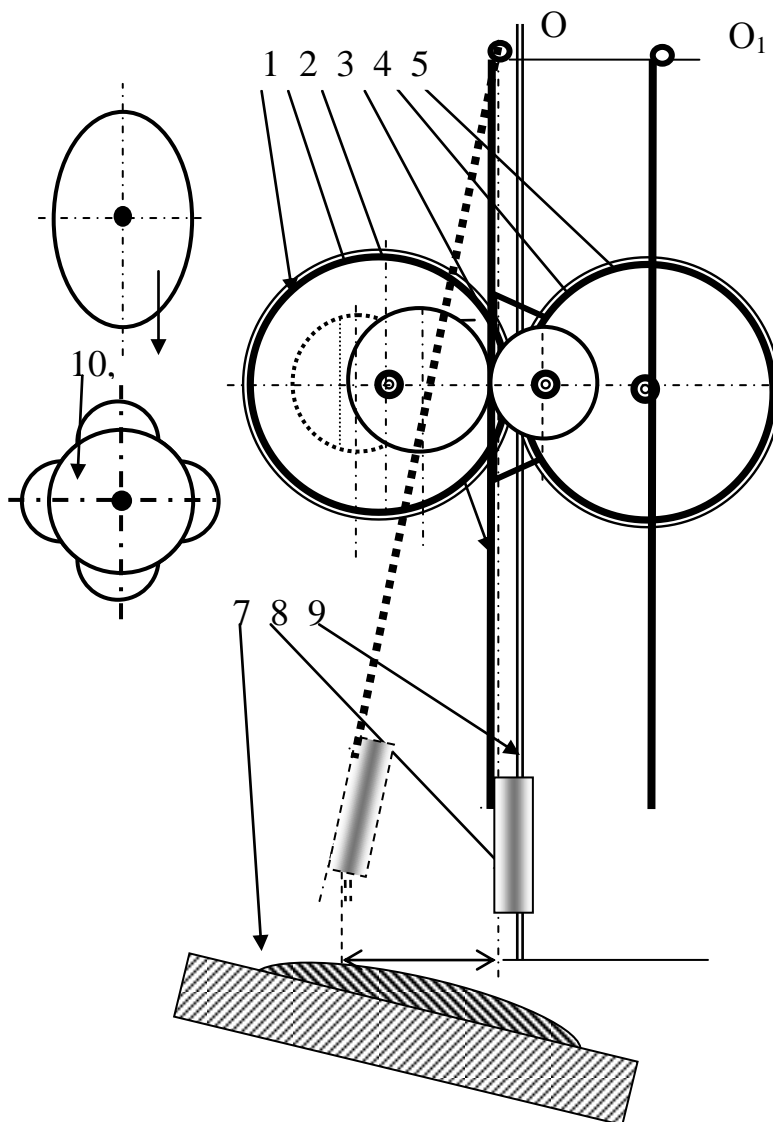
Вариант конструкции механизма подачи с колебателем от дополнительного ролика: 1- подающий ролик; 2 – ролик привода колебателя; 3 – рычаг колебателя; 4 – ролик колебателя; 5 – прижимной ролик; 6 – прижимной рычаг; 7 - изделие; 8 – сварочная горелка; 9 – электродная проволока; 10, 11 – варианты роликов возбудителей колебаний
